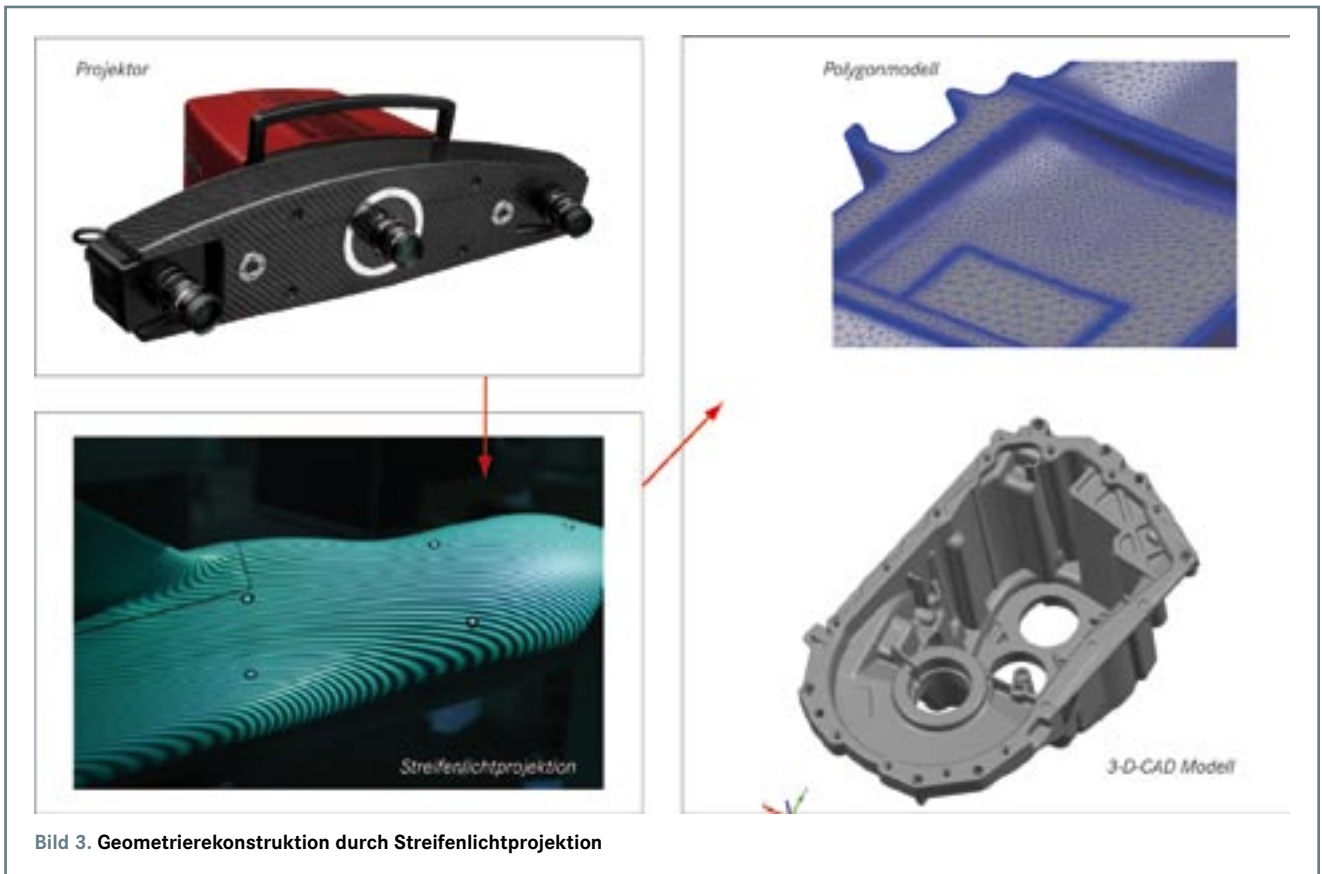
Geometrierekonstruktion durch Streifenlichtprojektion
